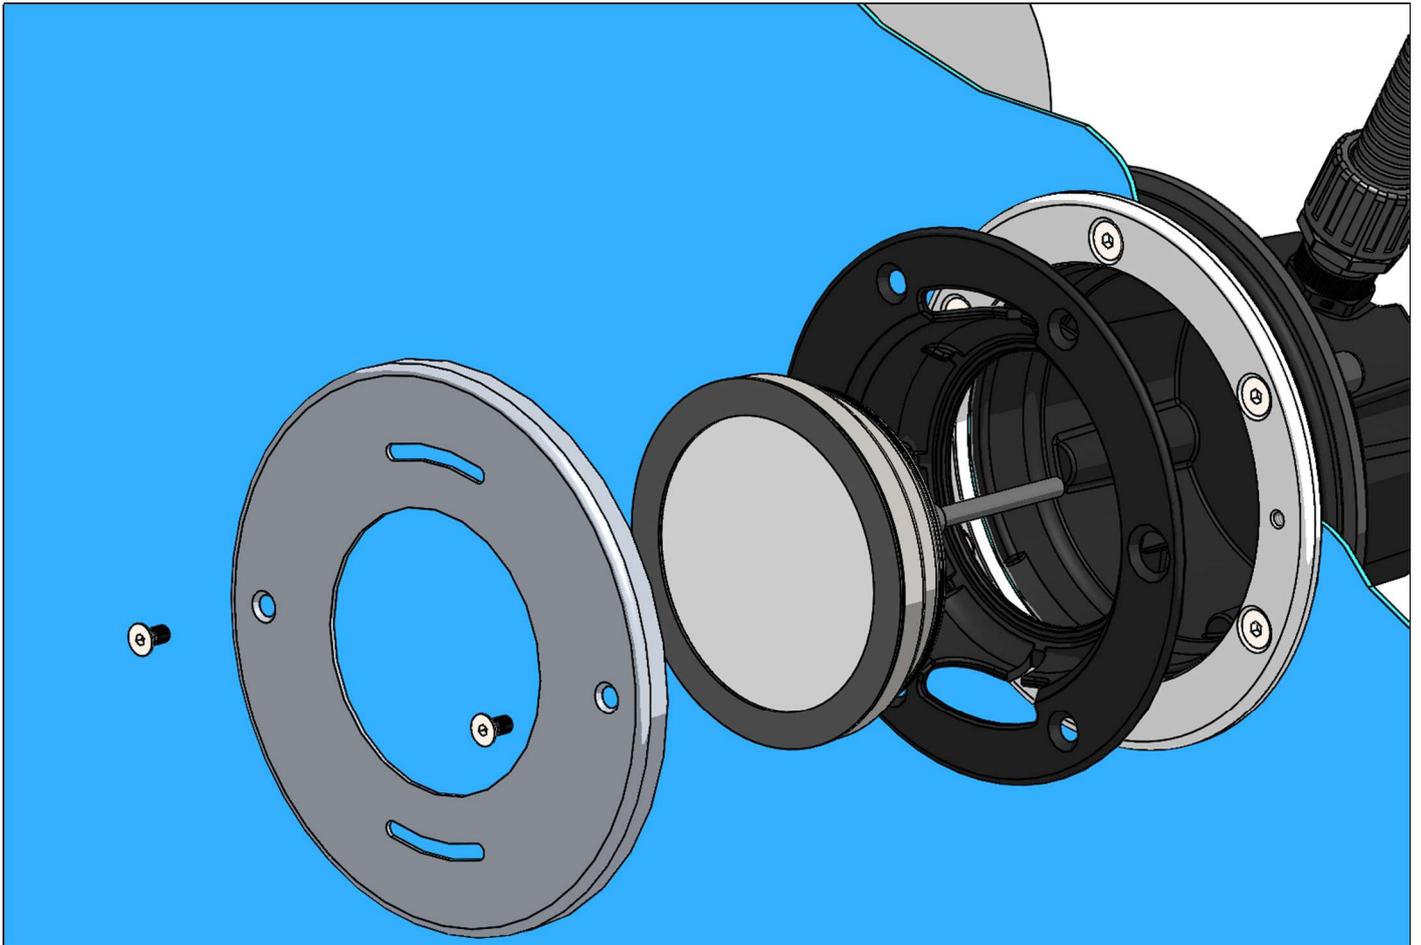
Fertigmontage Betonbecken mit Folienabdichtung
